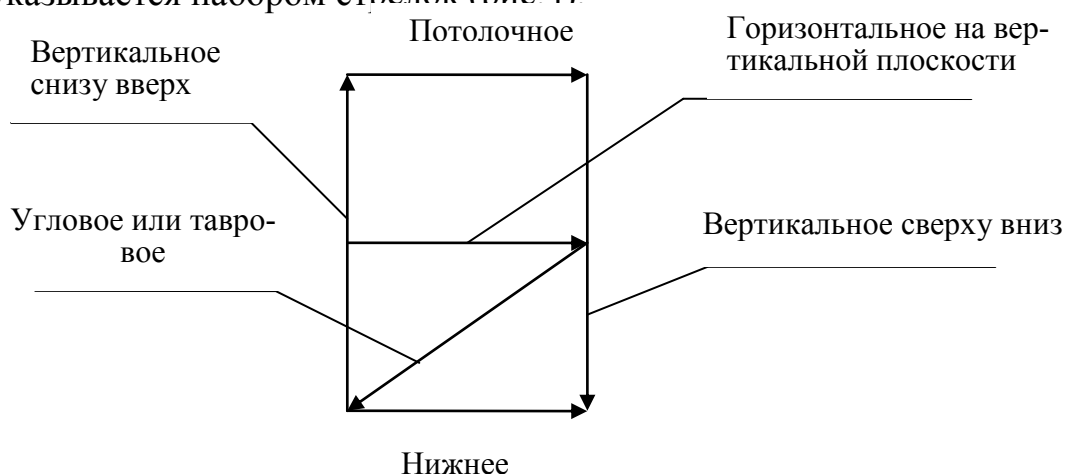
Графическое обозначение пространственных положений сварки
